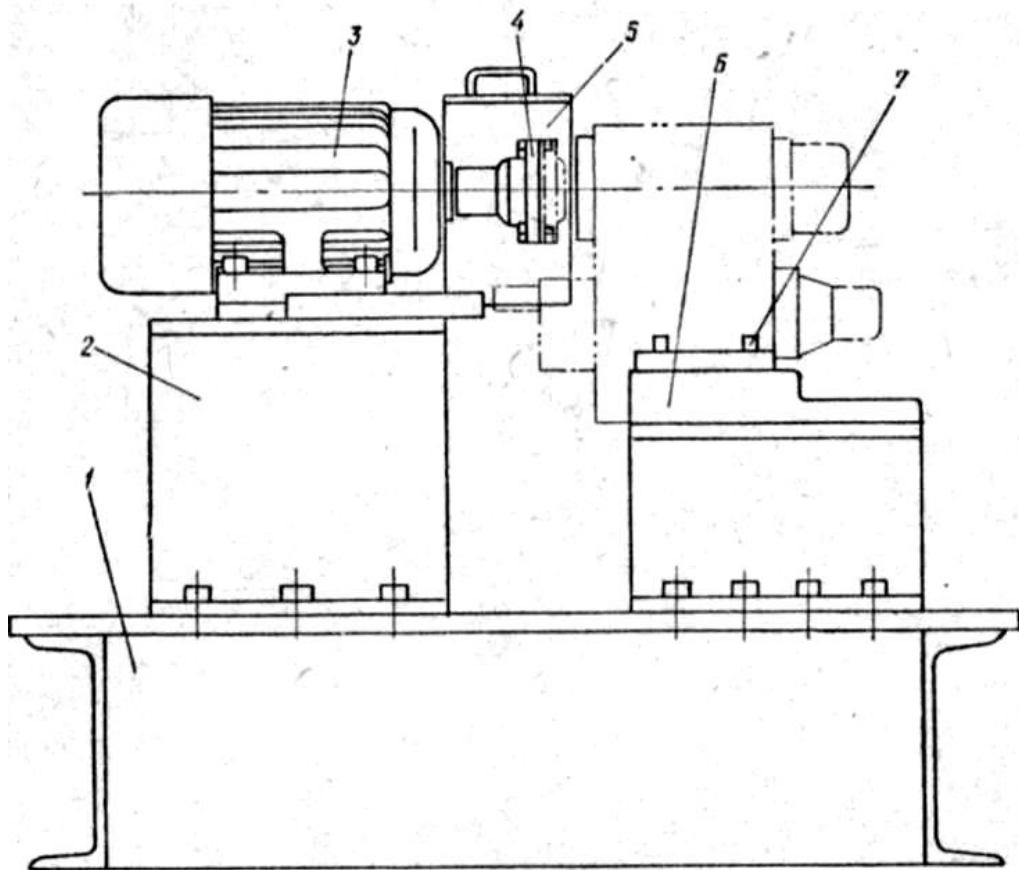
Схема станда для обкатки редуктора ВВП:
